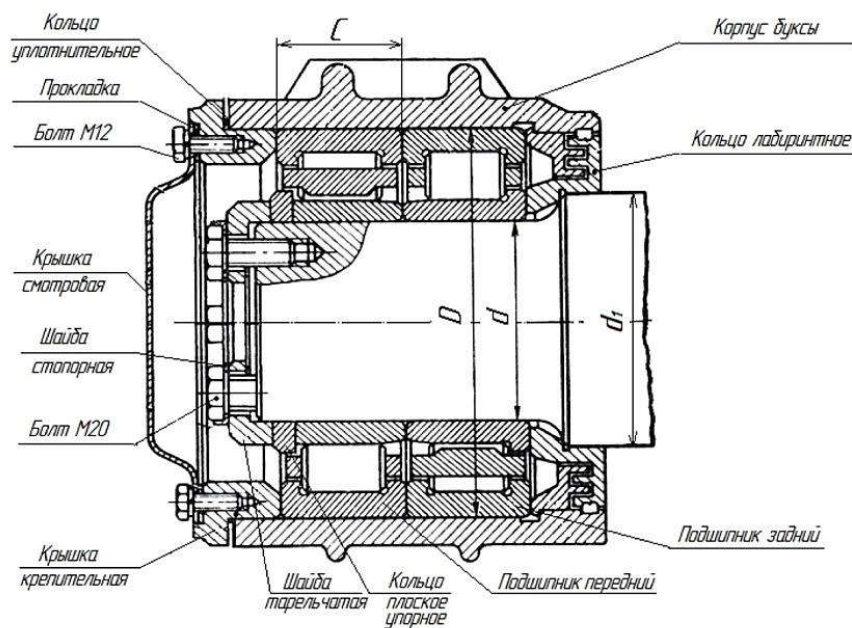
Буксовый узел с двумя подшипниками роликовыми цилиндрическими с торцевым креплением шайбой тарельчатой и болтами
